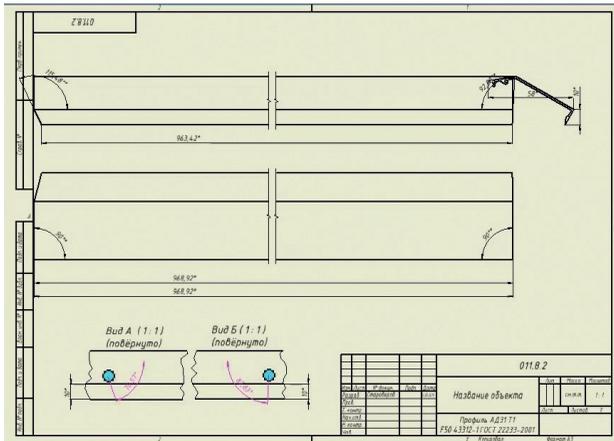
Чертеж детали Крышка после изменения параметрической 3D-модели фасада
